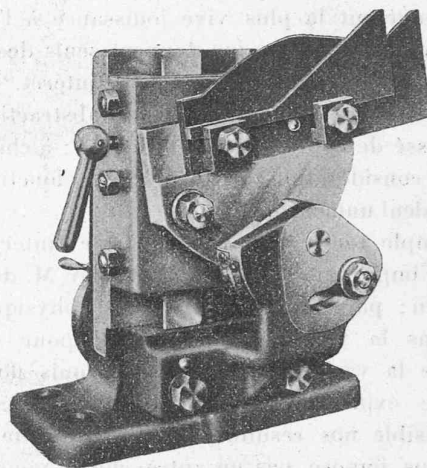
Porte-gabarit breveté de la machine à tailler les engrenages.
